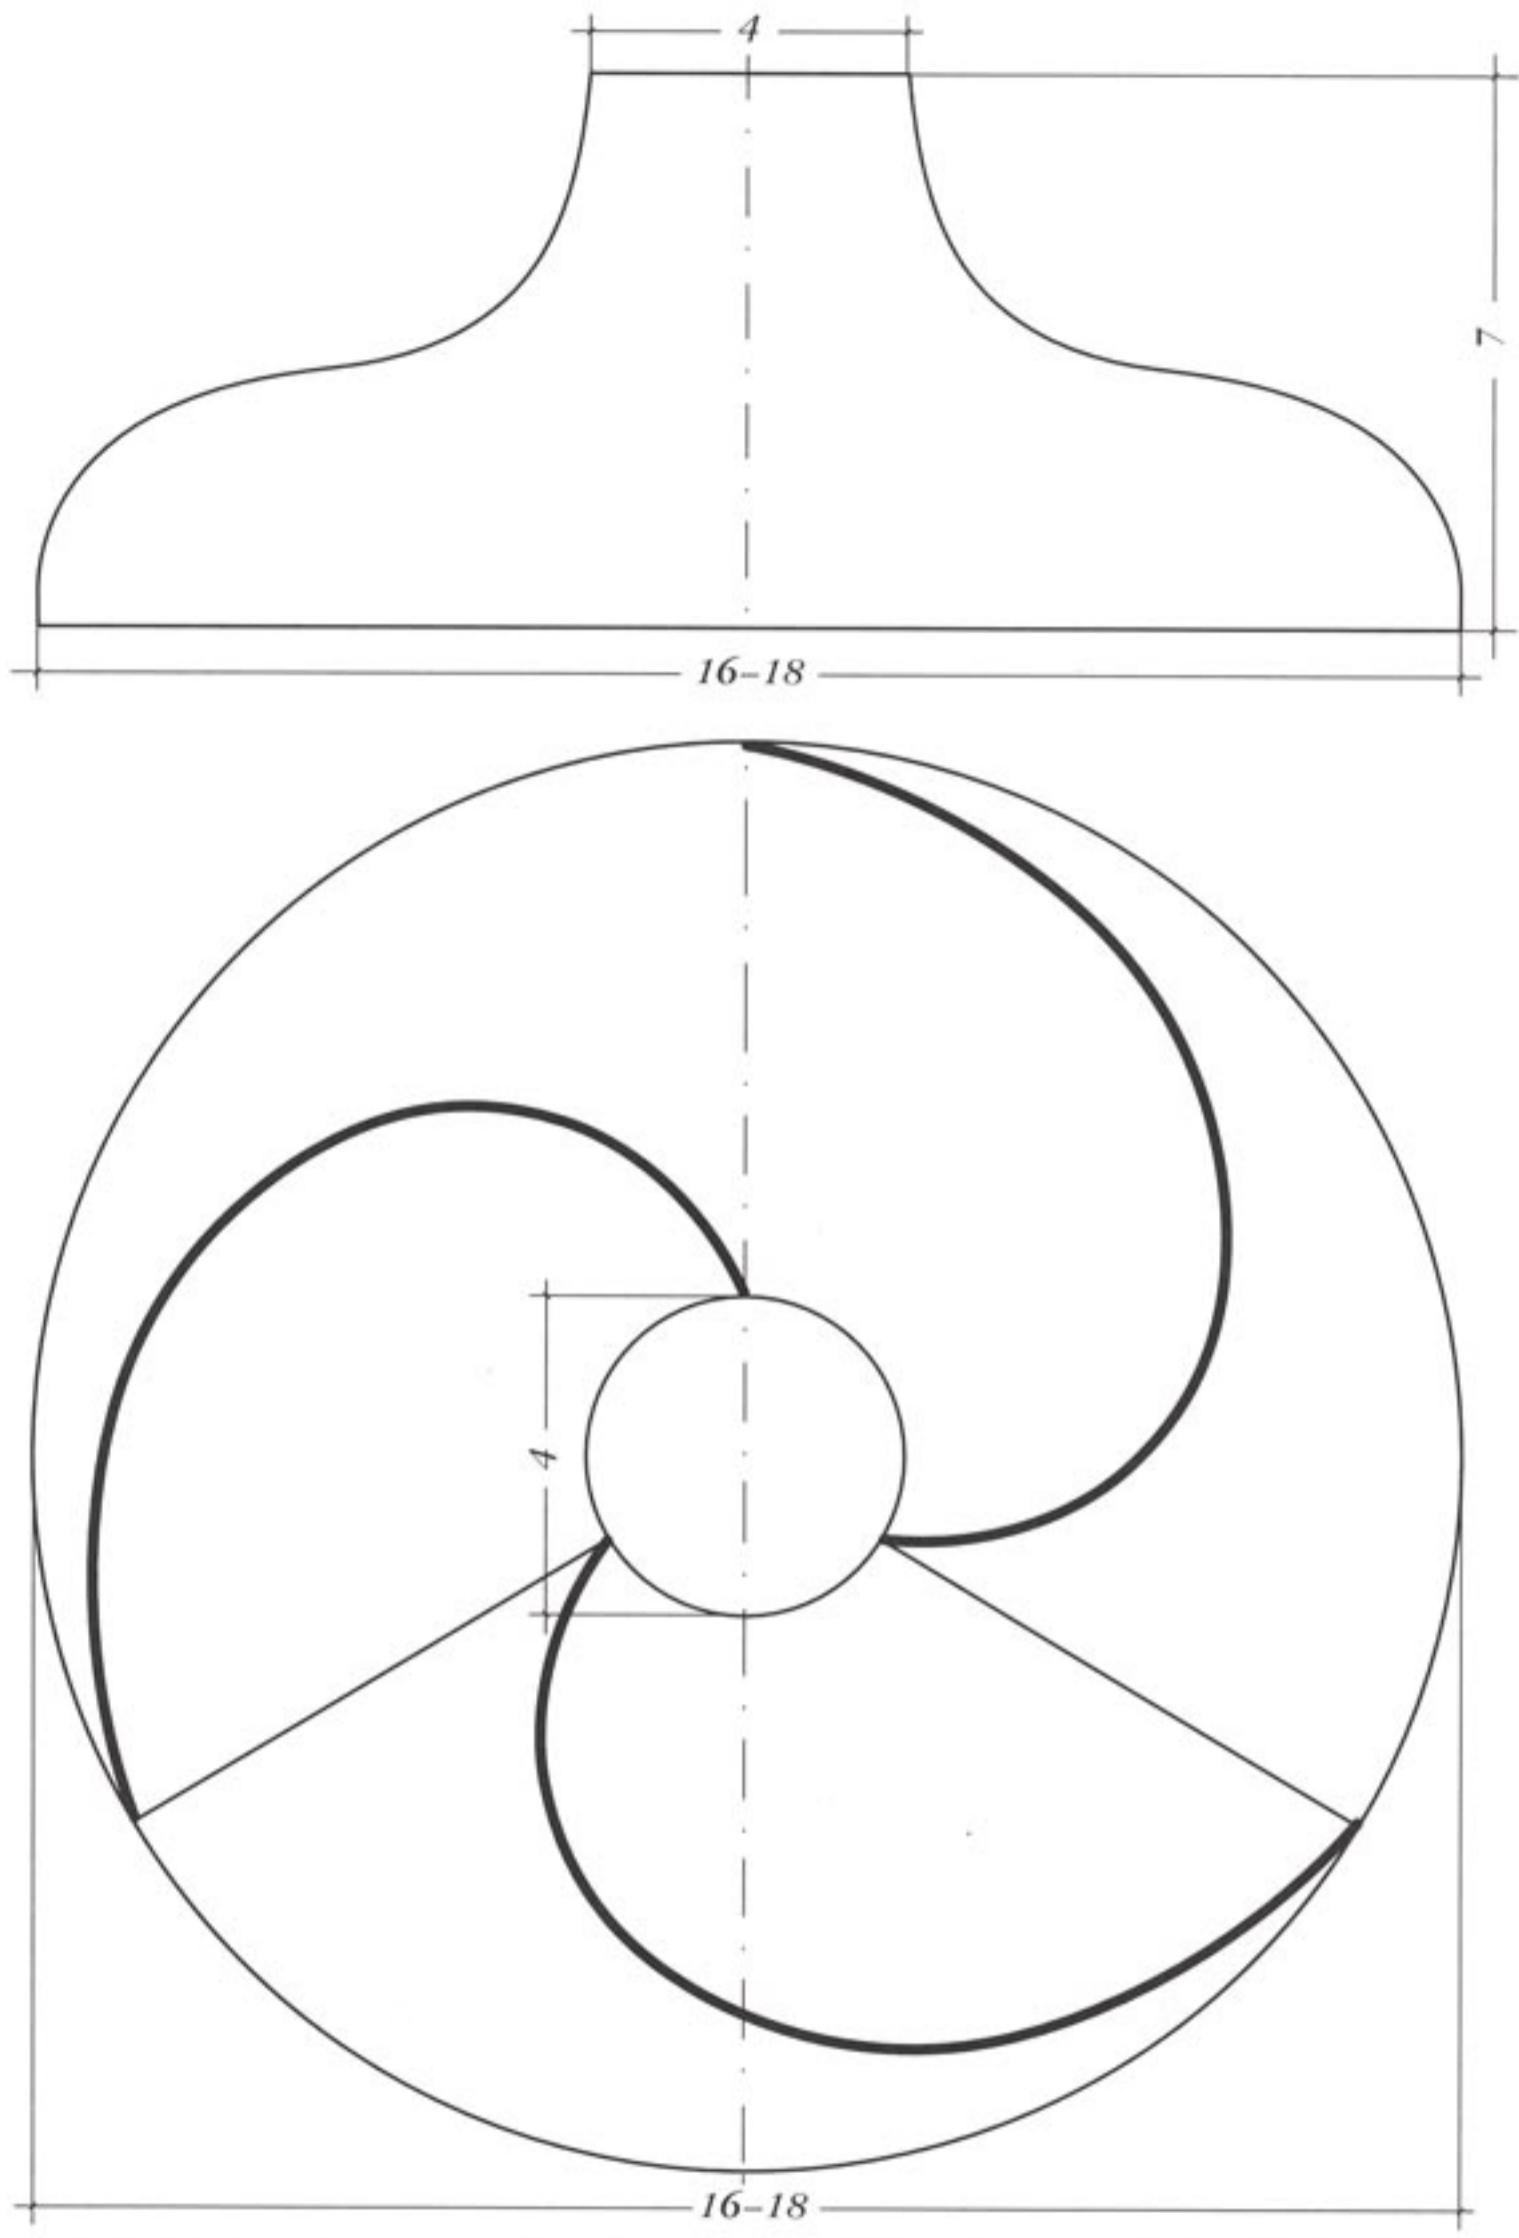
Чертеж и схема разметки основания четырехсвечника к рис. 184
